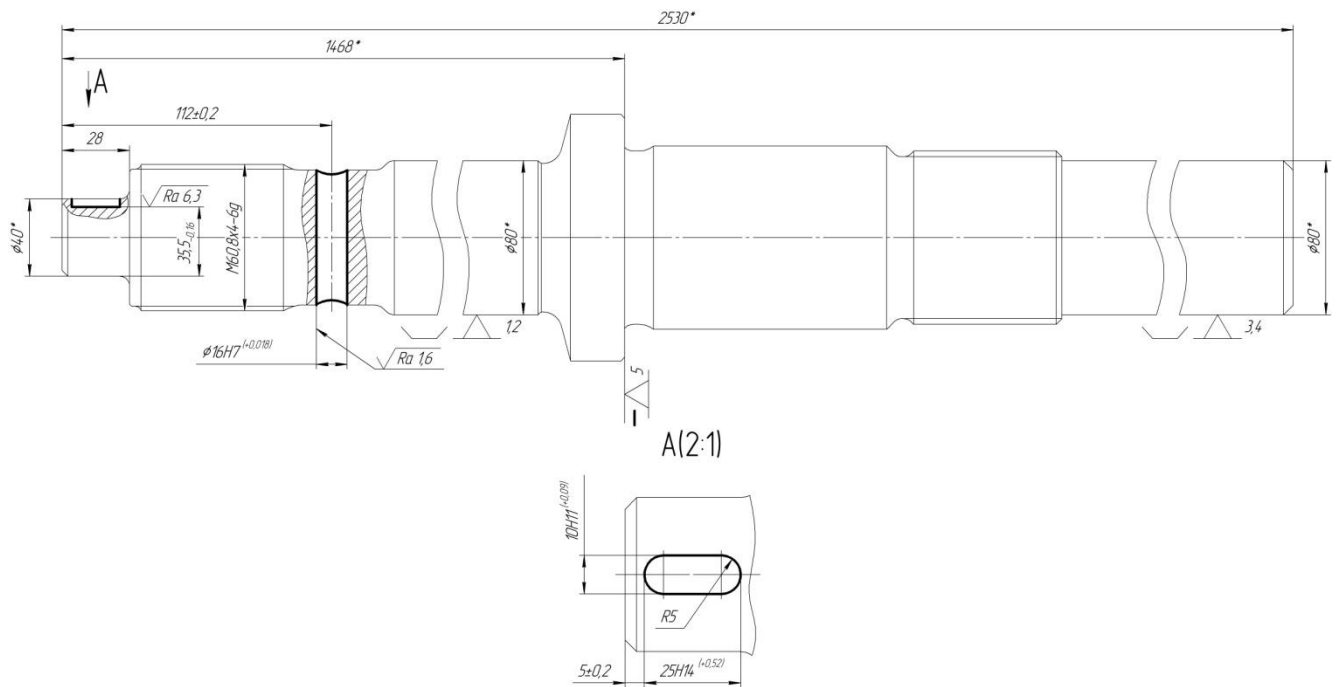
Схема базування заготовки на комплексній з ЧПК операції
